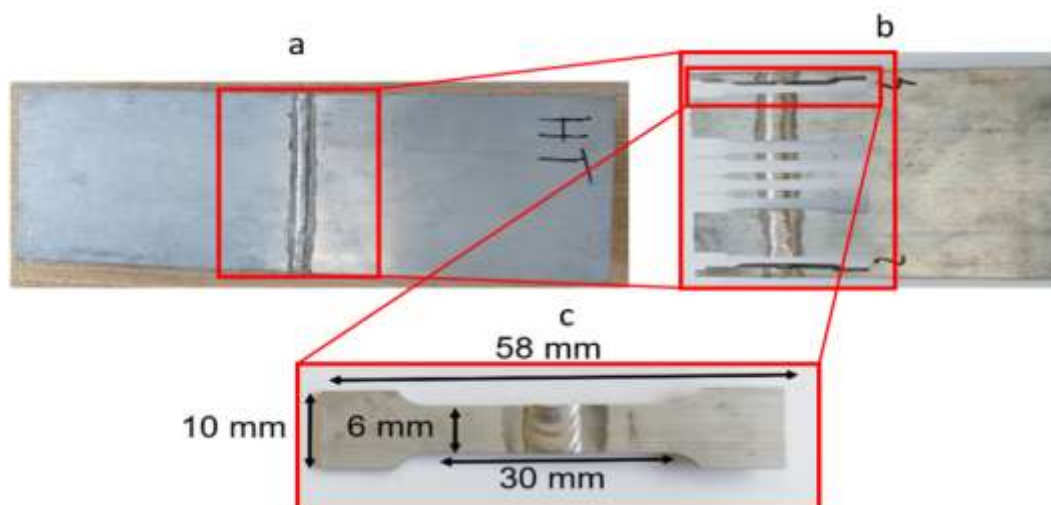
Étapes de prélèvement des éprouvettes. Portion de deck soudés bout à bout (a), deck après découpe (b), géométrie des éprouvettes prélevées (c).
